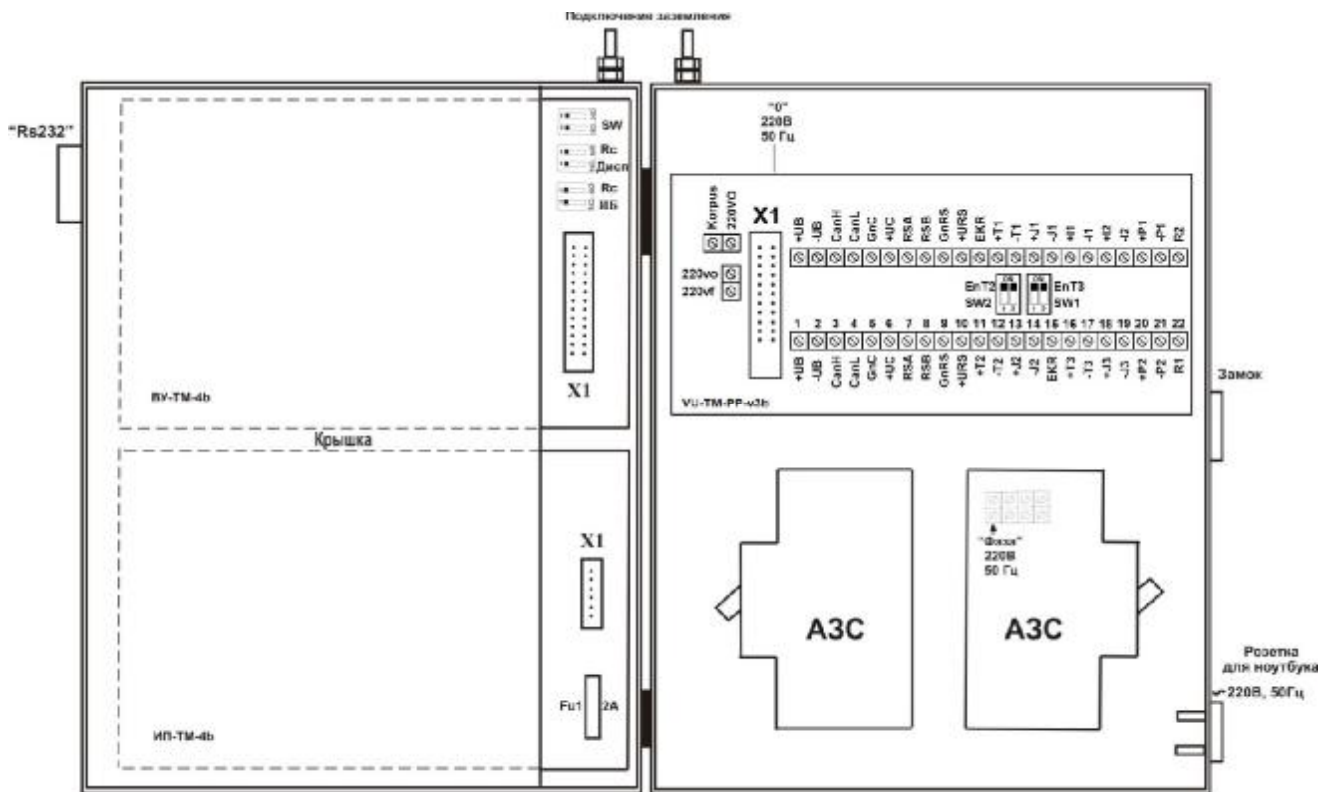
Габаритный чертеж и схема пломбирования ВУ.
